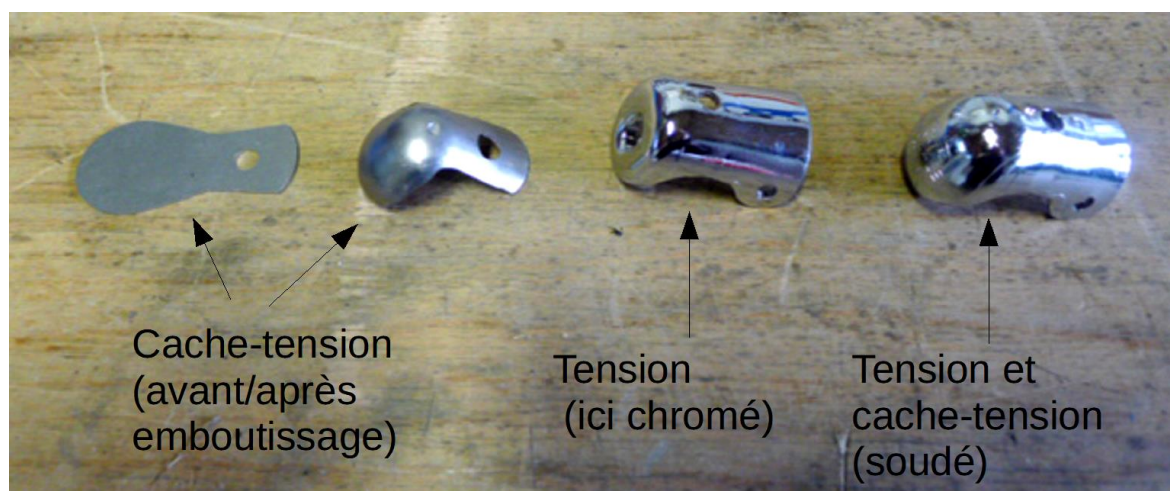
étapes de fabrication du bec constitué de la pièce « tension » et de la pièce « cache-tension »
